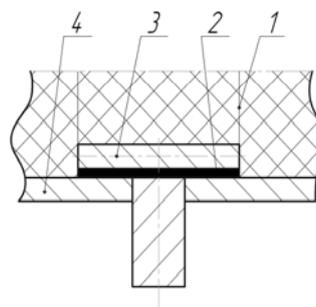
Подготовка образца: 1 – контур образца; 2 – резиновый уплотнитель; 3 – диск; 4 – днище
